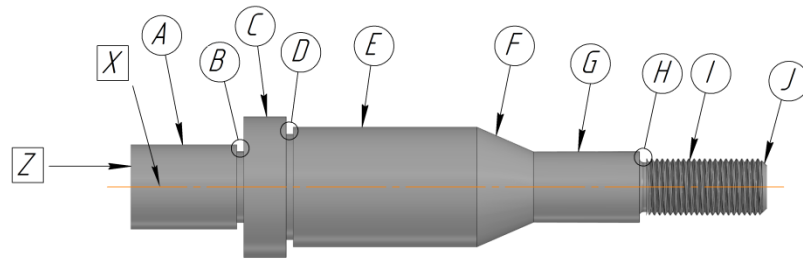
Класифікація поверхонь оброблюваної деталі
